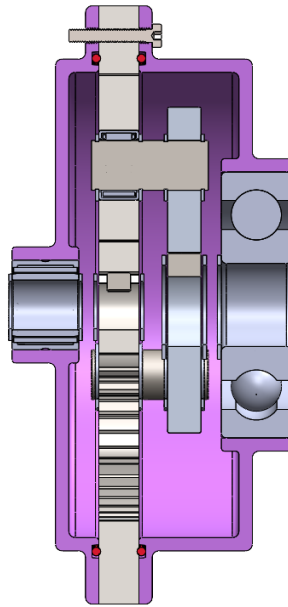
Vista en corte transversal del ensamblaje CAD 3D de la caja de engranes.
